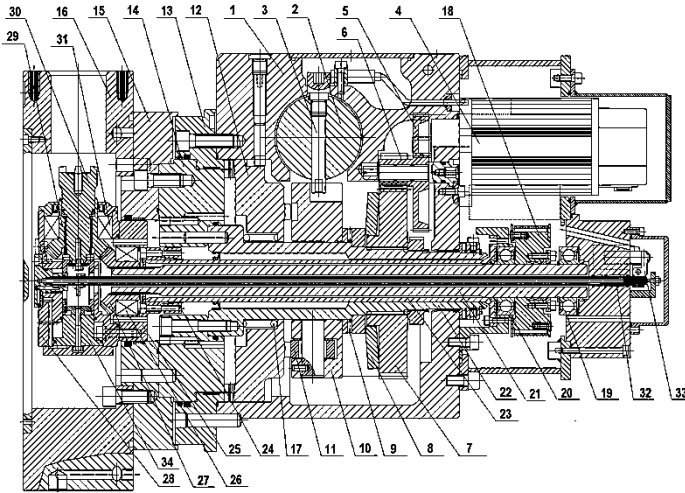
Револьверні головки токарних верстатів з ЧПК з приводом обертання інструмента
